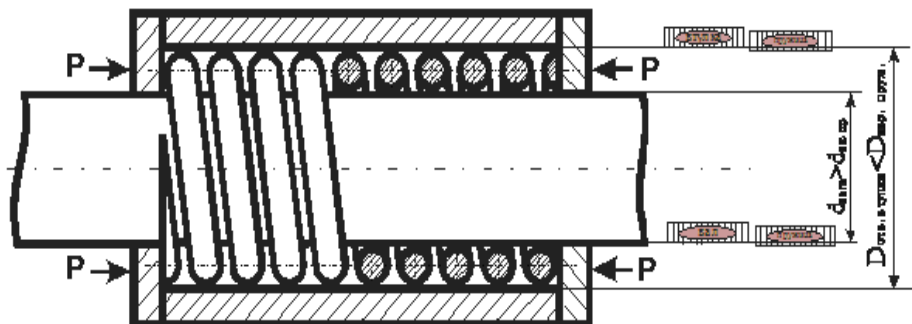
Схема посадок на рабочих поверхностях шарнирного подшипника с упругим пружинным вкладышем: подшипник находится в покое
